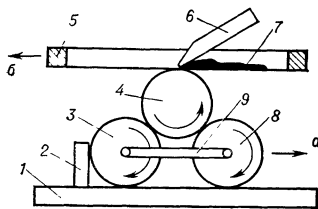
Устройство для этиографической печати на полимерных цилиндрах. Изделия: 1 — стол; 2 — тормозная стойка; 3 — цилиндр; 4 — изделие; 5 — печатная форма-трафарет; 6 — ракель; 7 — краска; 8 — цилиндр; 9 — соединительная пленка; а — направление движения цилиндра 3 и 8; б — направление движения формы-трафарета 5.
